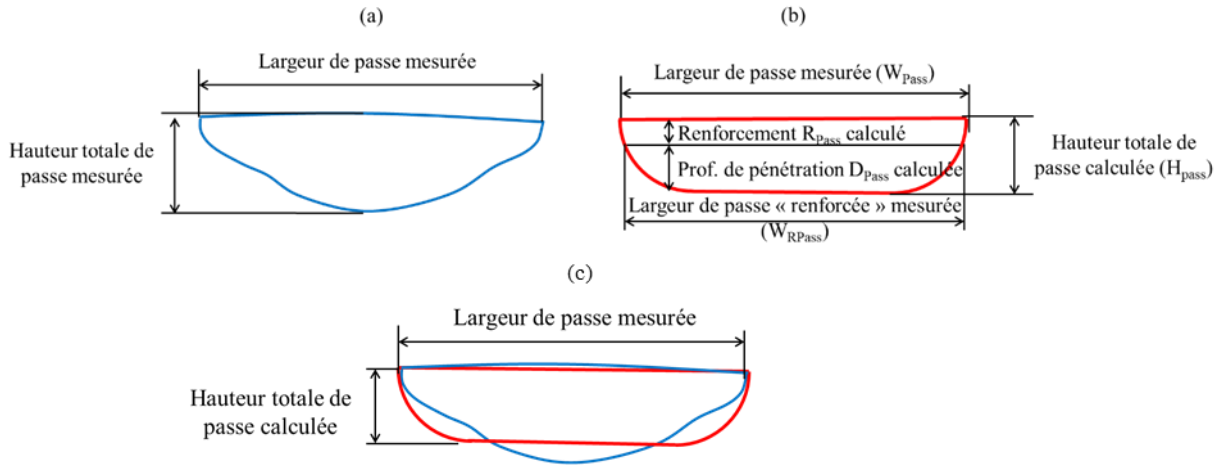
Forme et dimensions des passes observées (exemple de la dernière passe de la maquette Référence) (a), dimensions de la passe supposée « U-flat » (b) et superposition de la forme de passe observée à celle supposée « U-flat » (c).
